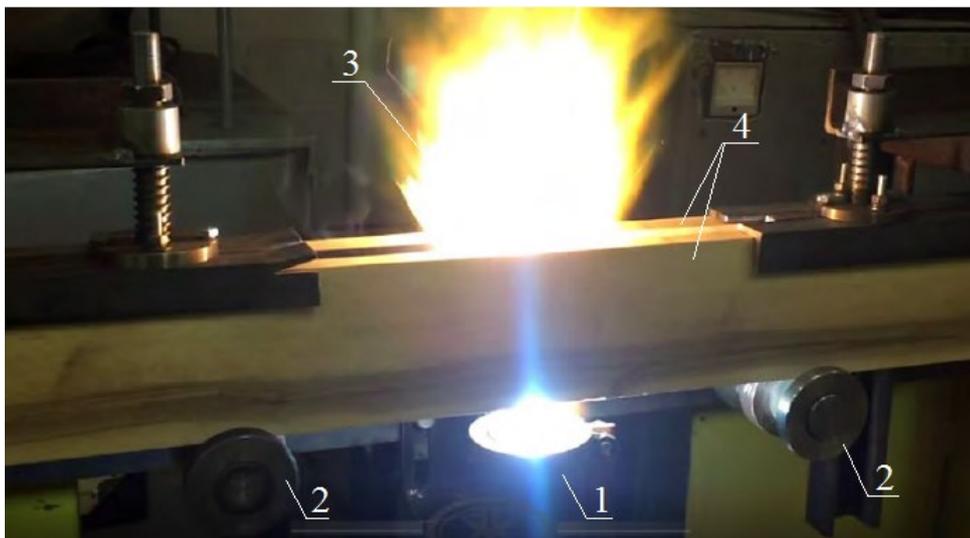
Фотография процесса плазменной обработки древесины: 1 – плазмотрон; 2 – ролики системы подачи обрабатываемых изделий; 3 – плазменный поток; 4 – обрабатываемые изделия
